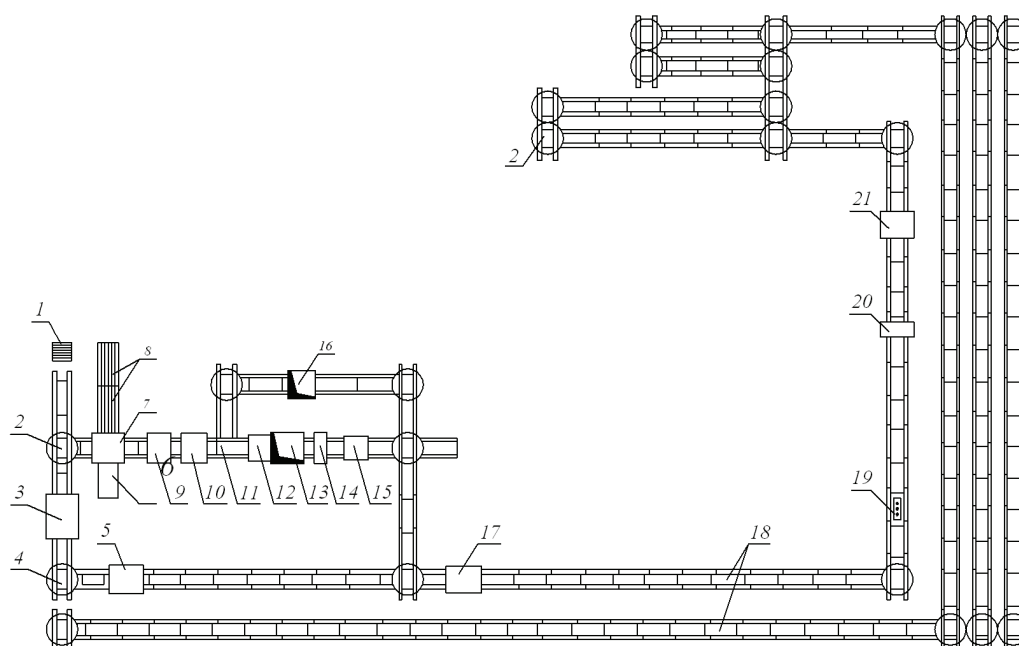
Планировка линии модели Л653С1: 1 – решетка выбивки бракованных форм; 2 – стол поворотный; 3 – распарщик; 4 – механизм съема формы с поддона; 5 – механизм очистки поддонов; 6 – сталкиватель кома; 7 – пресс выбивки; 8 – выбивные решетки; 9 – механизм очистки опок; 10 – кантователь; 11 – механизм сборки опок с подмодельной плиты; 12 – дозатор формовочной смеси; 13 – механизм встряхивания с прессованием; 14 – кантователь; 15 – механизм установки полуформ «низа» на поддон; 16 – бункер облицовочной смеси; 17 – механизм установки полуформ «низа» на поддон; 18 – рольганги; 19 – механизм фрезерования; 20 – кантователь; 21 – сборщик форм
